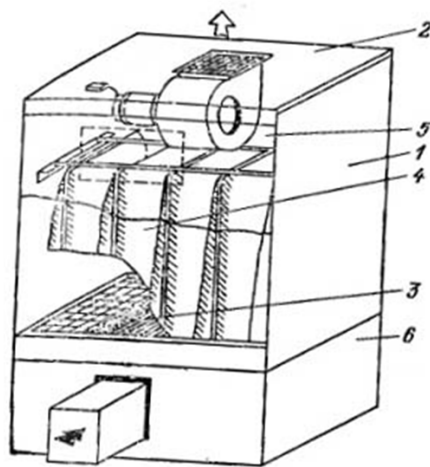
Низкоскоростной двухступенчатый туманоуловитель: 1 – корпус; 2 – крышка с вентилятором; 3 – первая ступень очистки; 4 – вторая ступень очистки; 5 – откидная дверца; 6 – маслосборник²⁸
